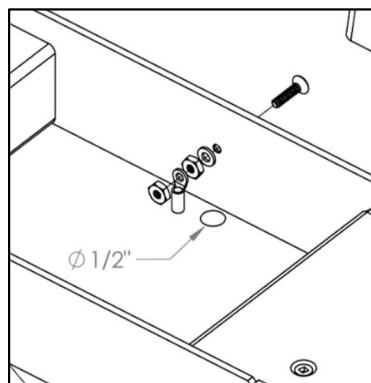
Assemblage du connecteur et trou de passage du fil d'alimentation des rails
